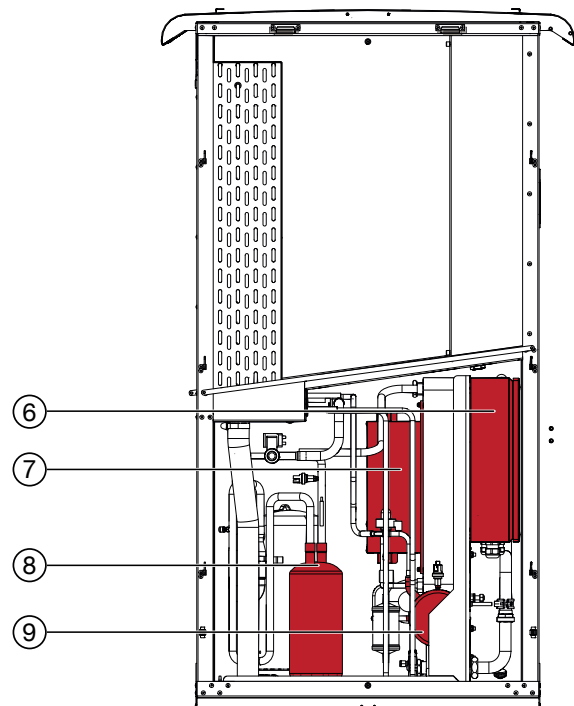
Wärmepumpe Seitenansicht geöffnet
